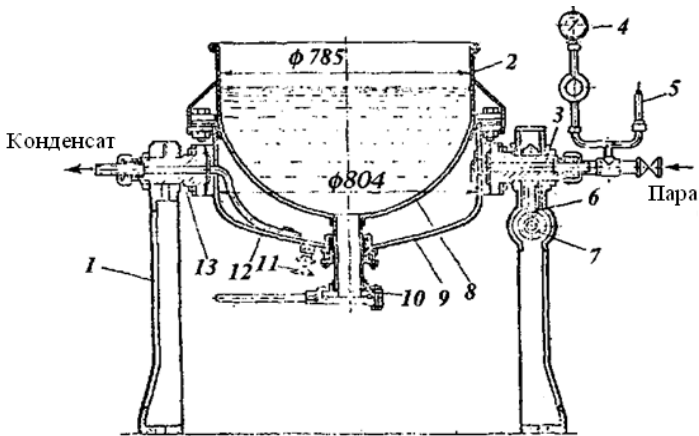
Котел підігрівач Д9-41А: 1 – стояк; 2 – обичайка; 3, 13 – цапфи; 4 – манометр; 5 – запобіжний клапан; 6 – черв'ячне колесо; 7 – черв'як; 8 – мідна чаша; 9 – оболонка; 10 – патрубок із затвором; 11 – вентиль; 12 – труба для конденсату.
